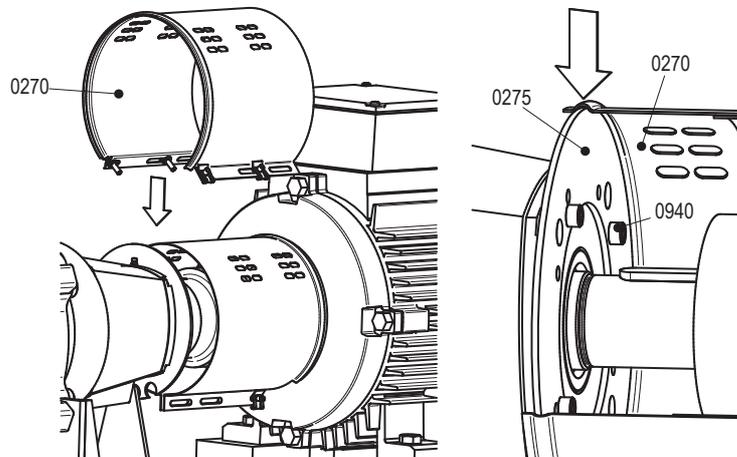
Montieren des Mantels auf der Pumpenseite.
